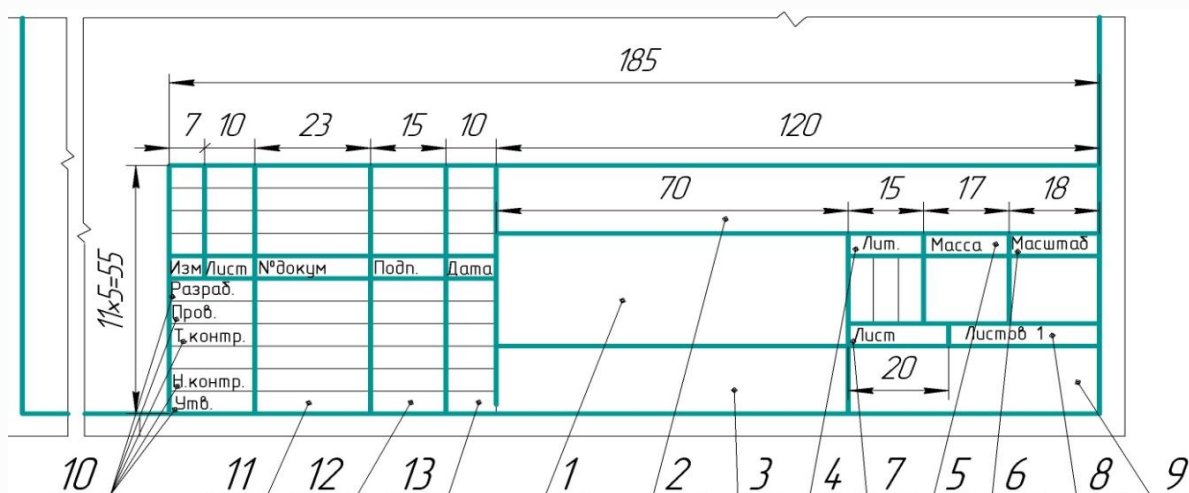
Форма 1 ГОСТ 2.104-2006 – для чертежей и схем
